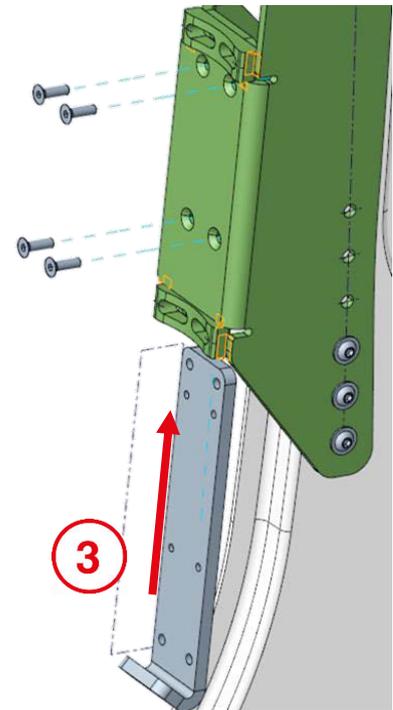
Montage Gewindeplatte; Ansicht Außenseite
